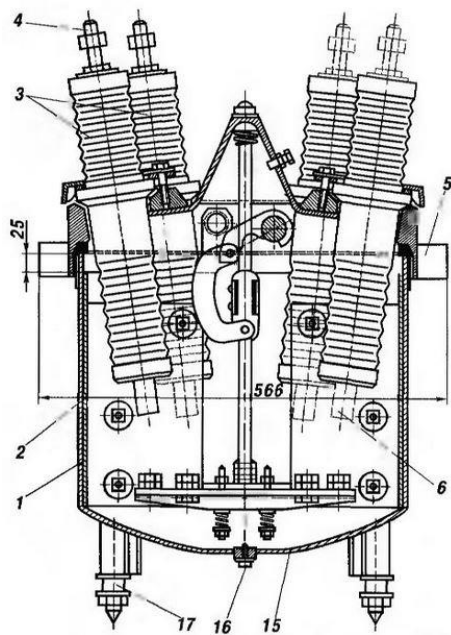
Конструкция бакового масляного выключателя.
